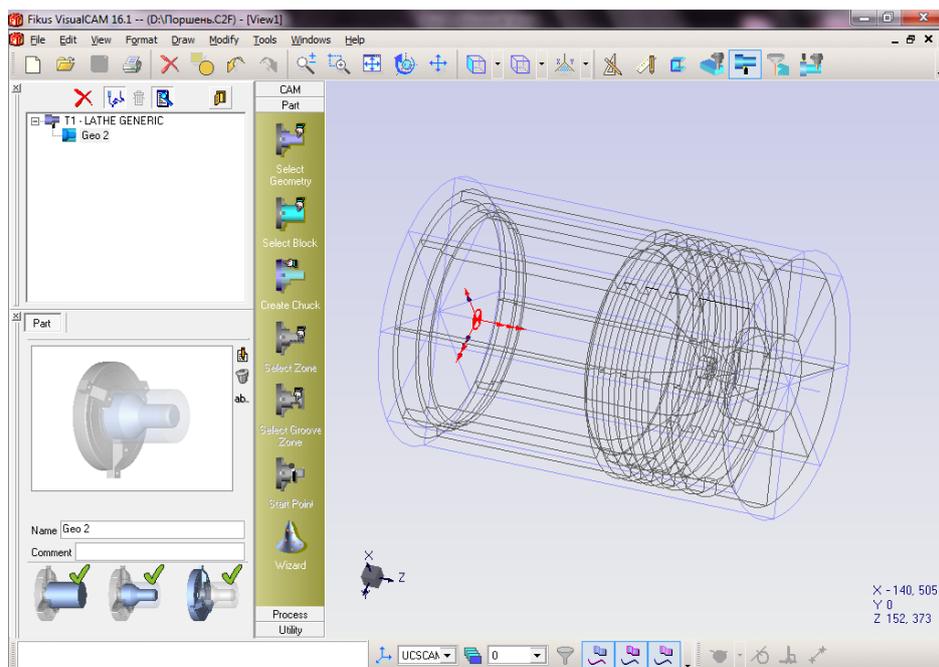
Отображение заготовки (Поршень.c2f)
